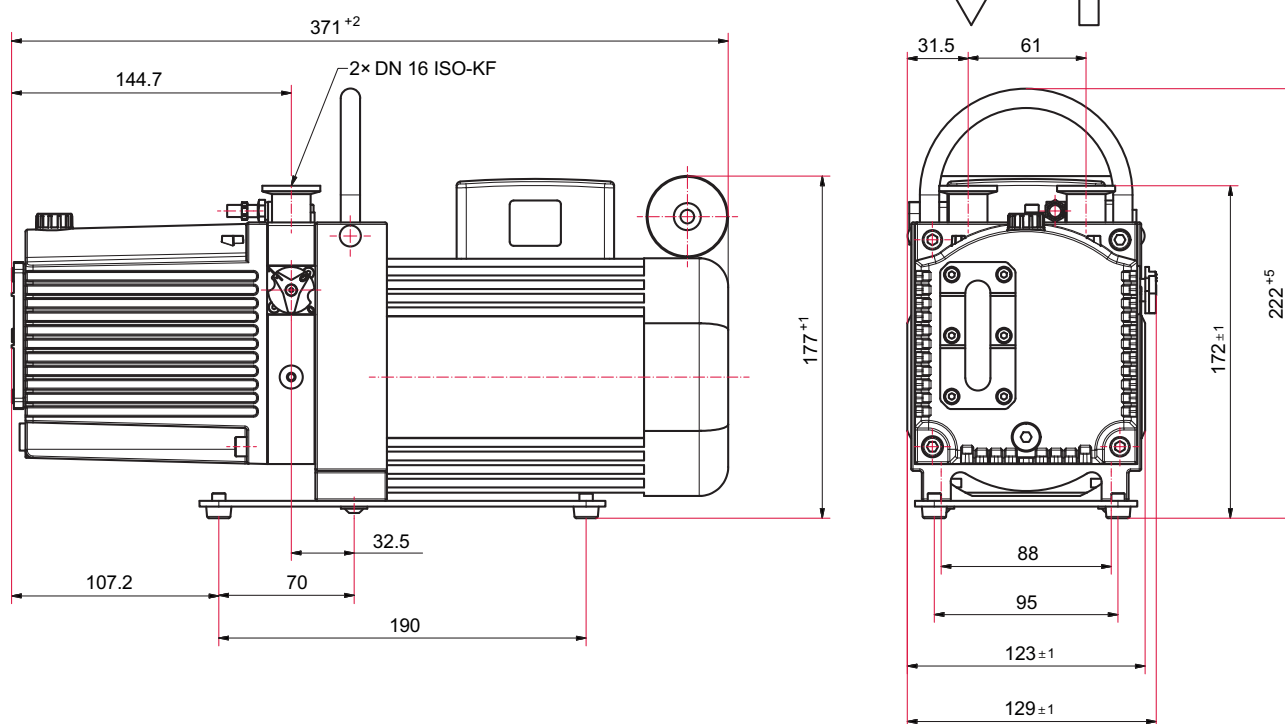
Dimensões do Duo 6, motor monofásico, 230–240 V, 50/60 Hz
